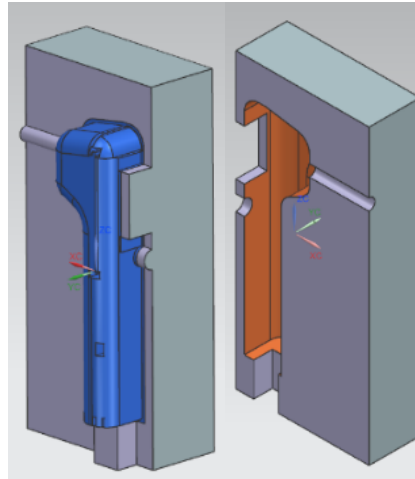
a) Placa de corazón del componente izquierdo b) Placa de cavidad del componente izquierdo.
